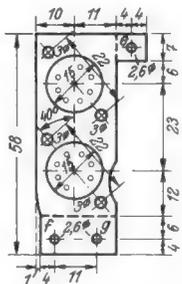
Trägerblech für Röhrenfassungen (Aluminiumblech 0,5 mm)
